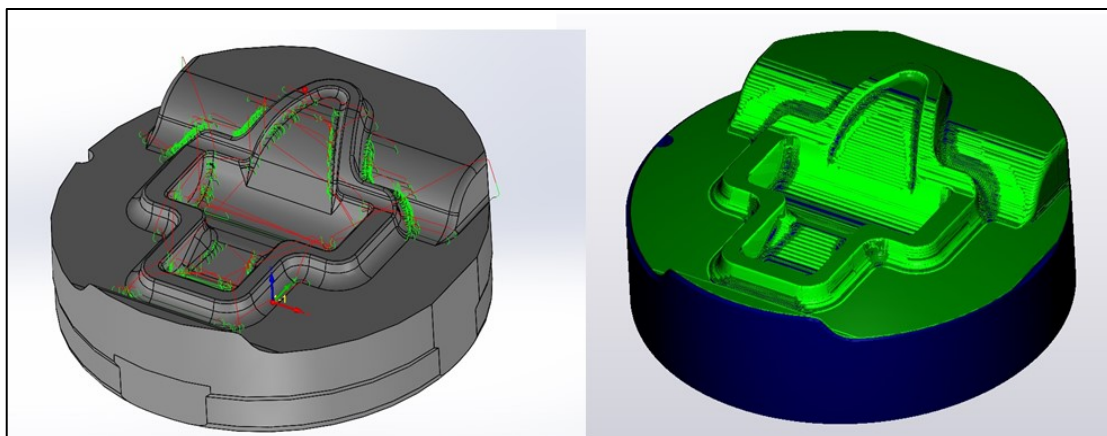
Dráhy hrubování D8, kontrola přídavků po hrubování
